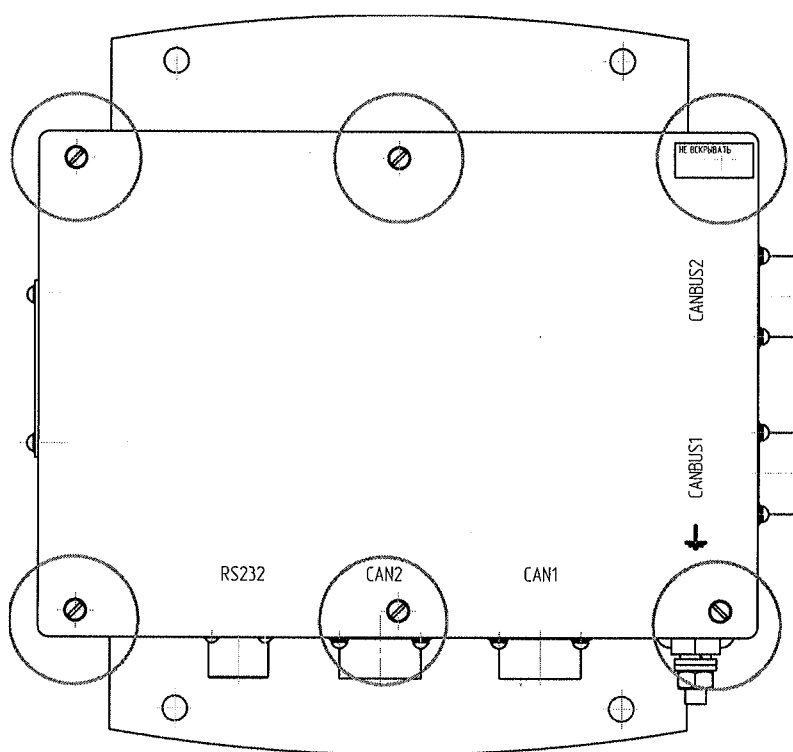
Внешний вид блока Шлюз CAN
